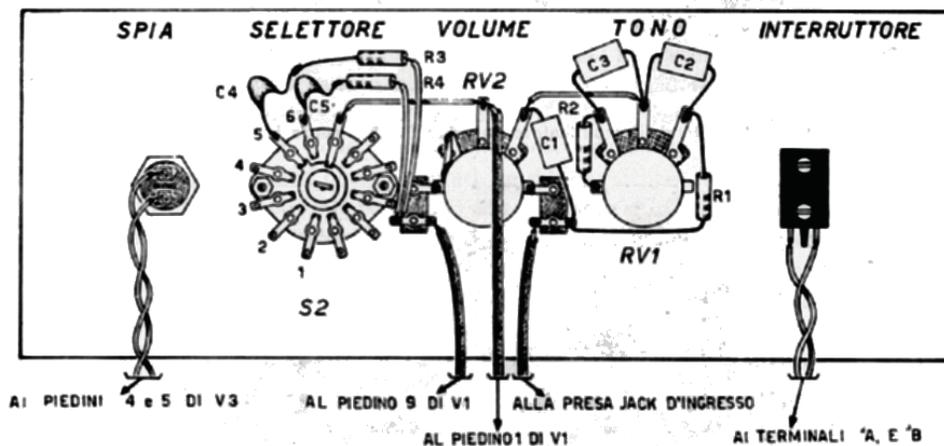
Disposizione dei componenti dietro il pannello frontale.
